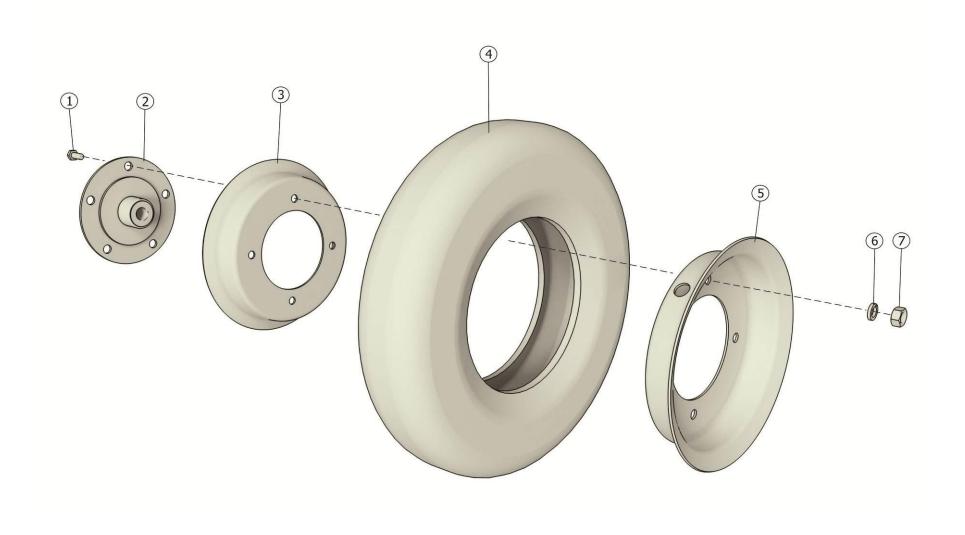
Колесо в сборе МЗС-90.01.100
